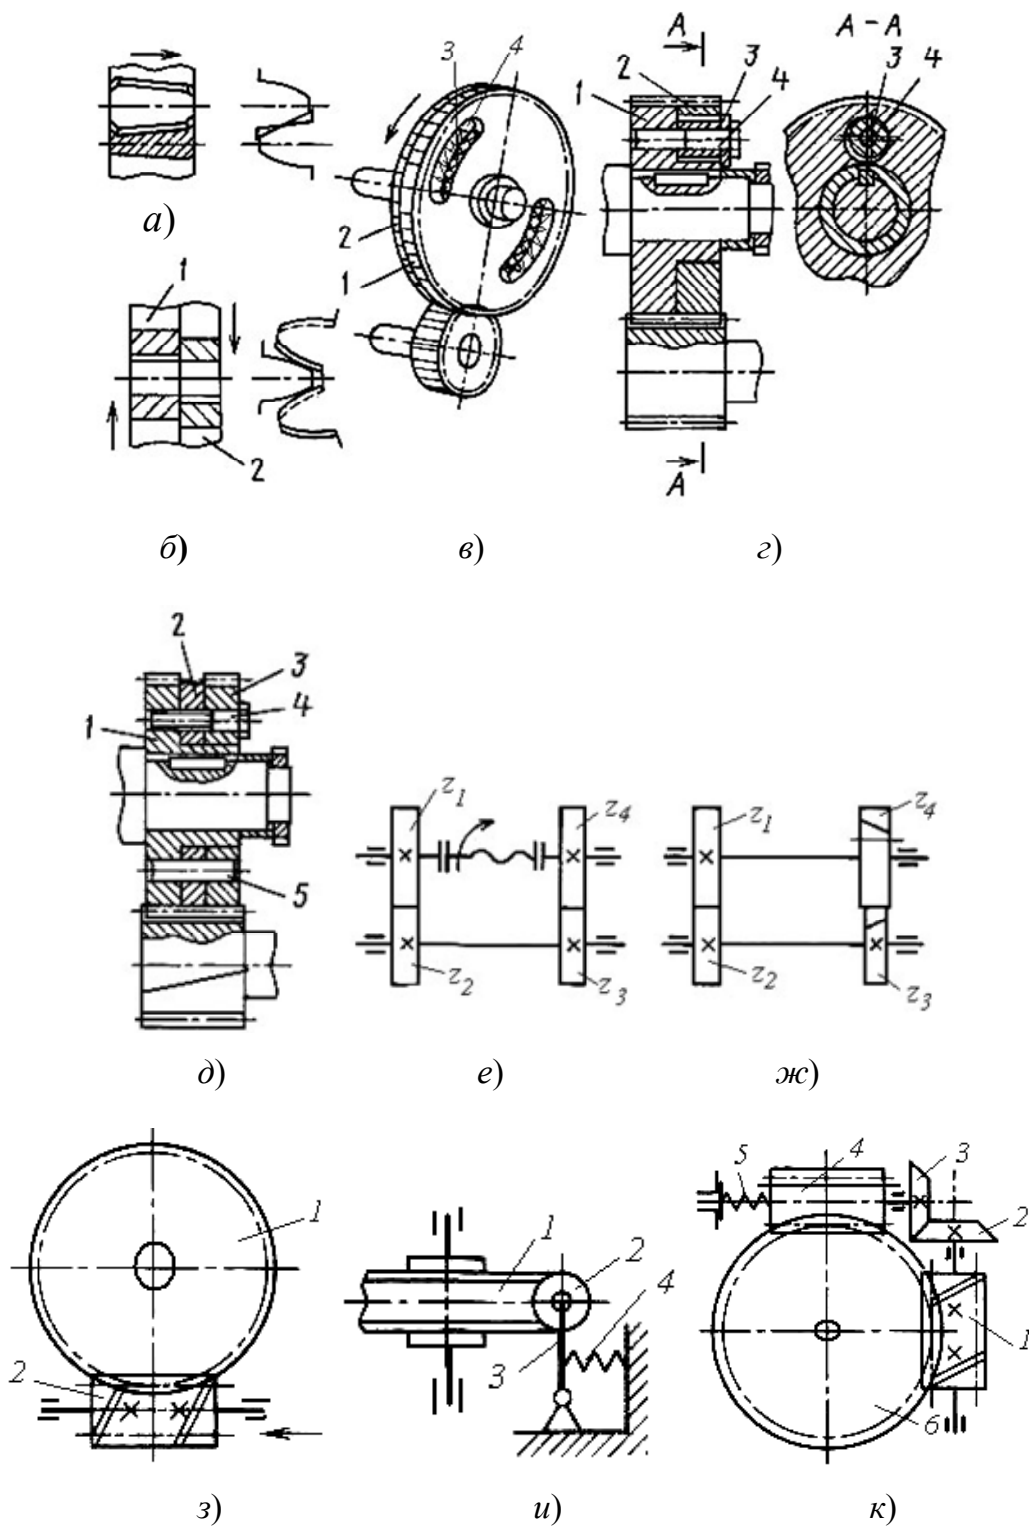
Способы компенсации боковых зазоров в зубчатых передачах:
